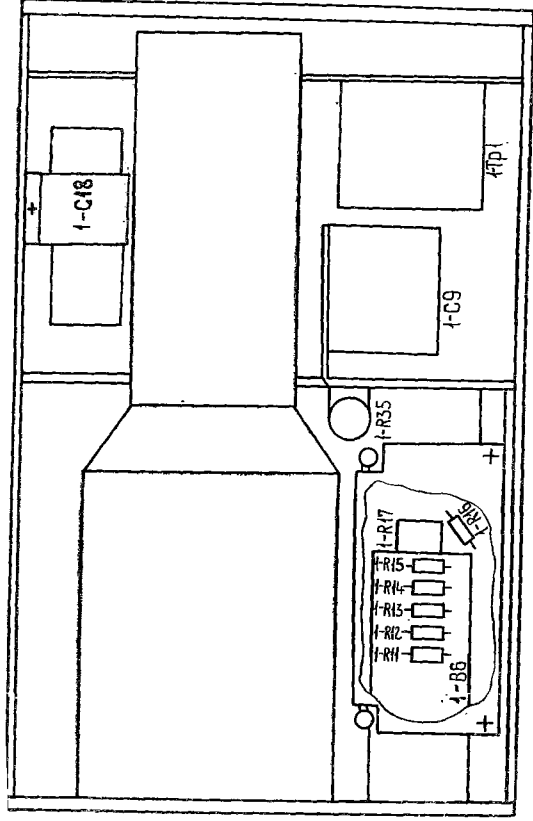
Схема расположения установочных элементов и печатной платы (вид сверху).
